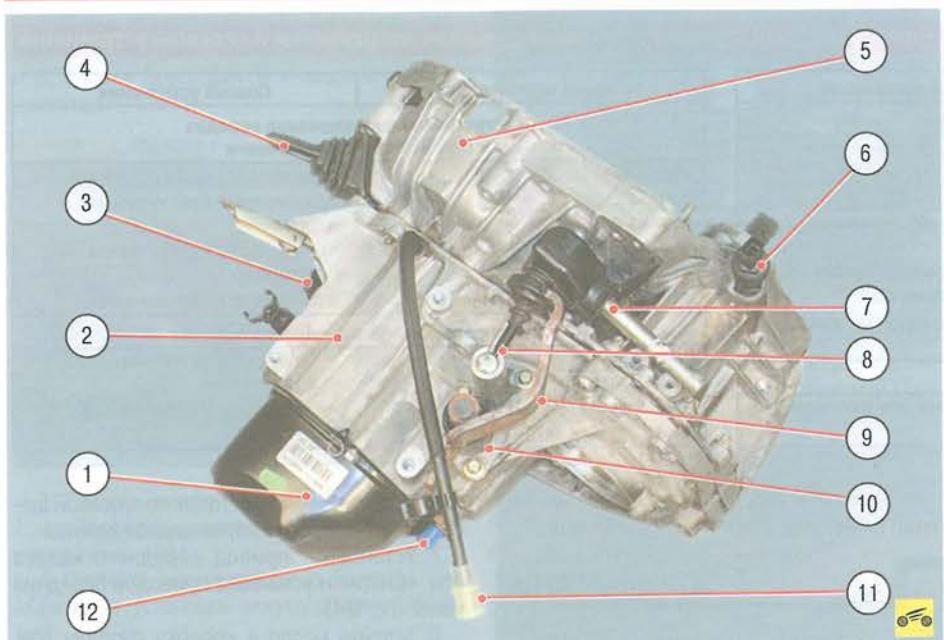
Коробка передач: 1 – задняя крышка; 2 – картер коробки передач; 3 – пробка наливного отверстия; 4 – вилка выключения сцепления; 5 – картер сцепления; 6 – датчик скорости; 7 – рычаг управления коробкой передач; 8 – шток выбора передач; 9 – рычаг переключения передач; 10 – механизм переключения передач; 11 – сапун; 12 – выключатель света заднего хода
